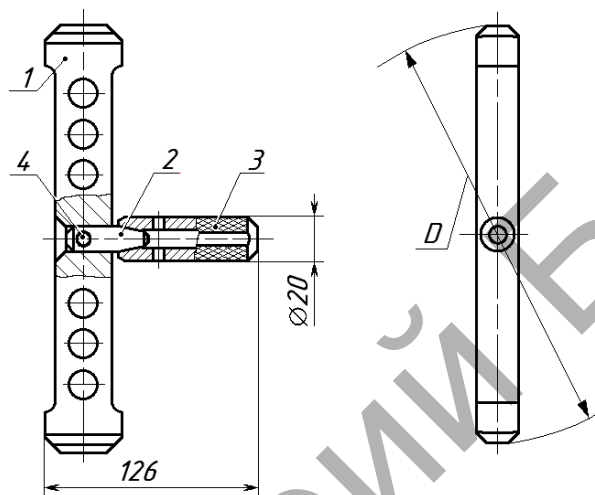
Конструкция гладкого проходного неполного калибра-пробки $D_{\text{номин.}} = 125$ мм для контроля отверстия с полем допуска $H7$
